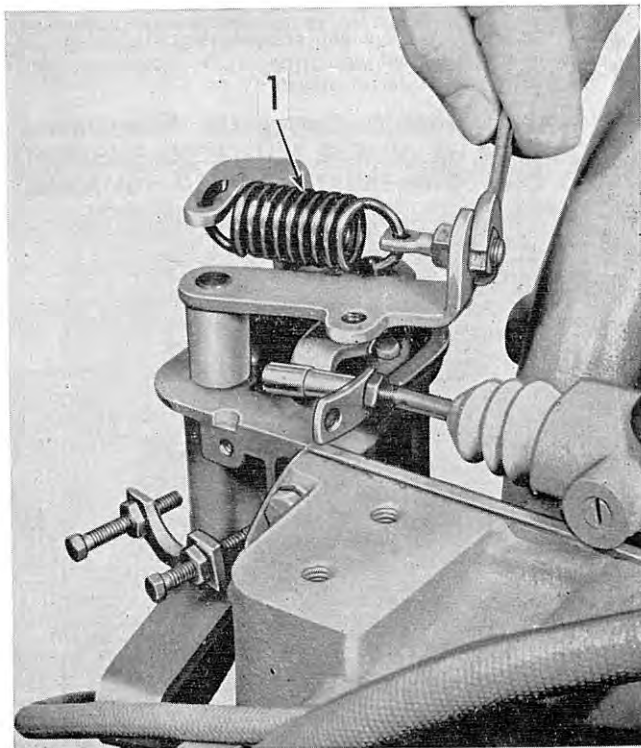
Réglage par la tige à œillet du ressort du régulateur
